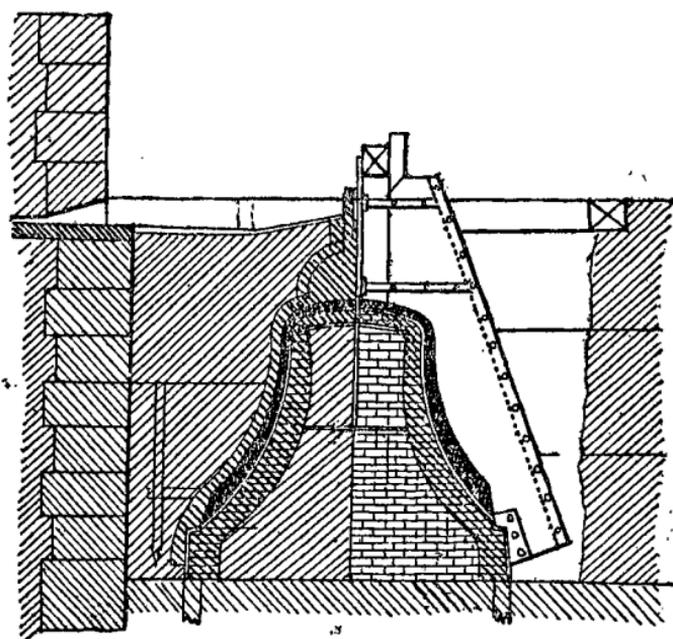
Moulage d'une cloche. Troussage de la fausse pièce : à gauche, moule avec la charge *p* braquée sur la fausse pièce.
